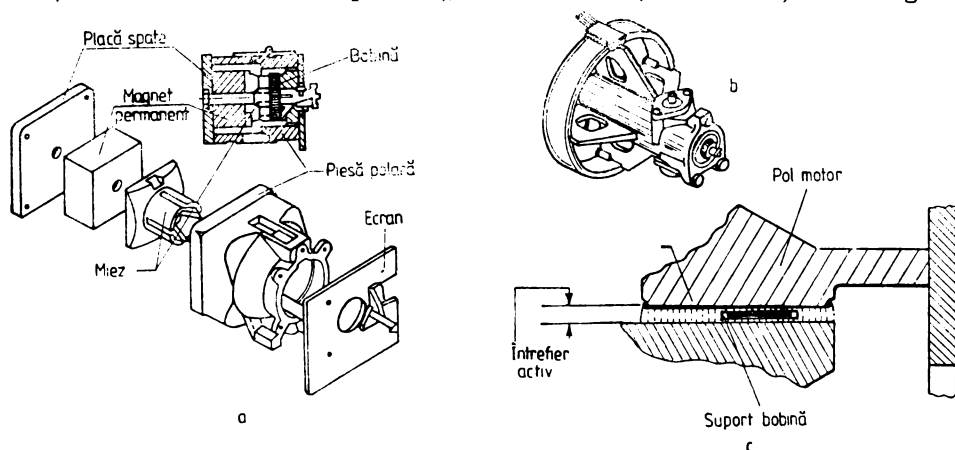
Motor linear cu bobină scurtă pentru unitățile „data module“ (IBM 3340):
